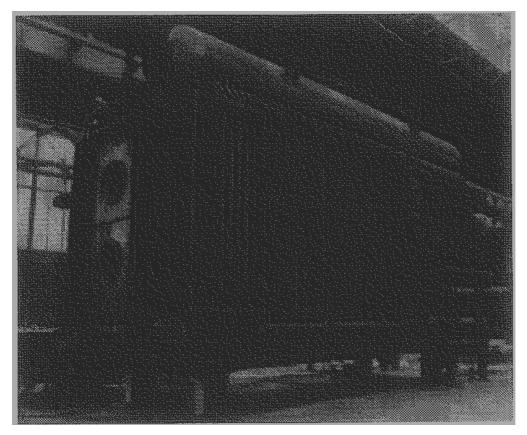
Vue de face d'une chaudière à tubes d'eau
